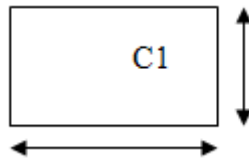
Dimensions mínimes dels contactes d'una targeta PLUG-IN SIM.
